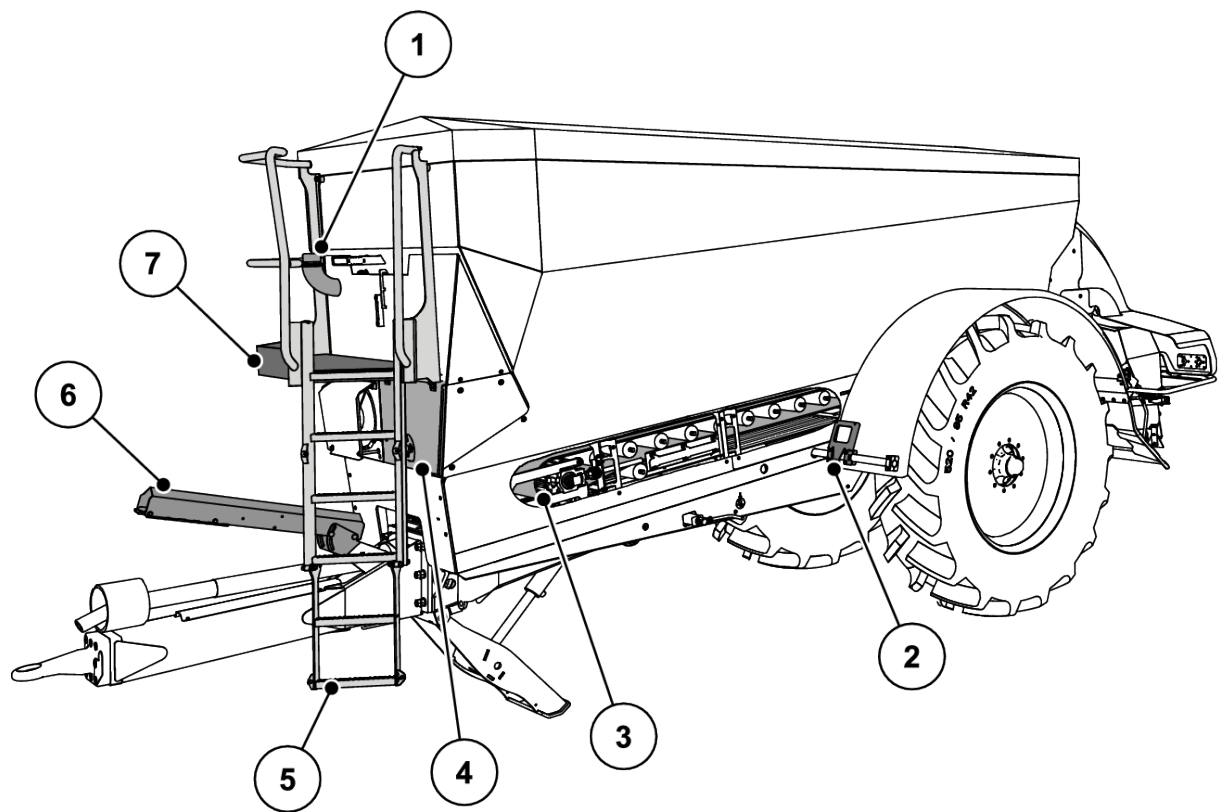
Vedere generală a subansamblurilor: Partea frontală
